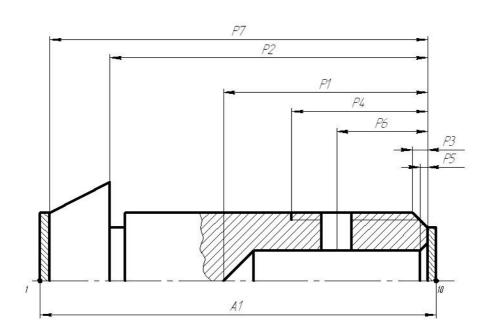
Эскиз детали с условными обозначениями размеров
